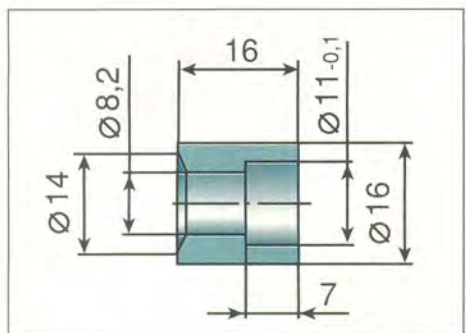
Оправка для запрессовки направляющей втулки клапанов ВАЗ.
